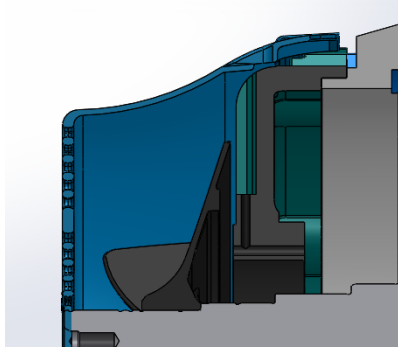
Posição 1 (Ventilador Padrão 420x134, Cota P = 31 mm, Cota H = 6 mm, Cota F = 30.74 mm)
